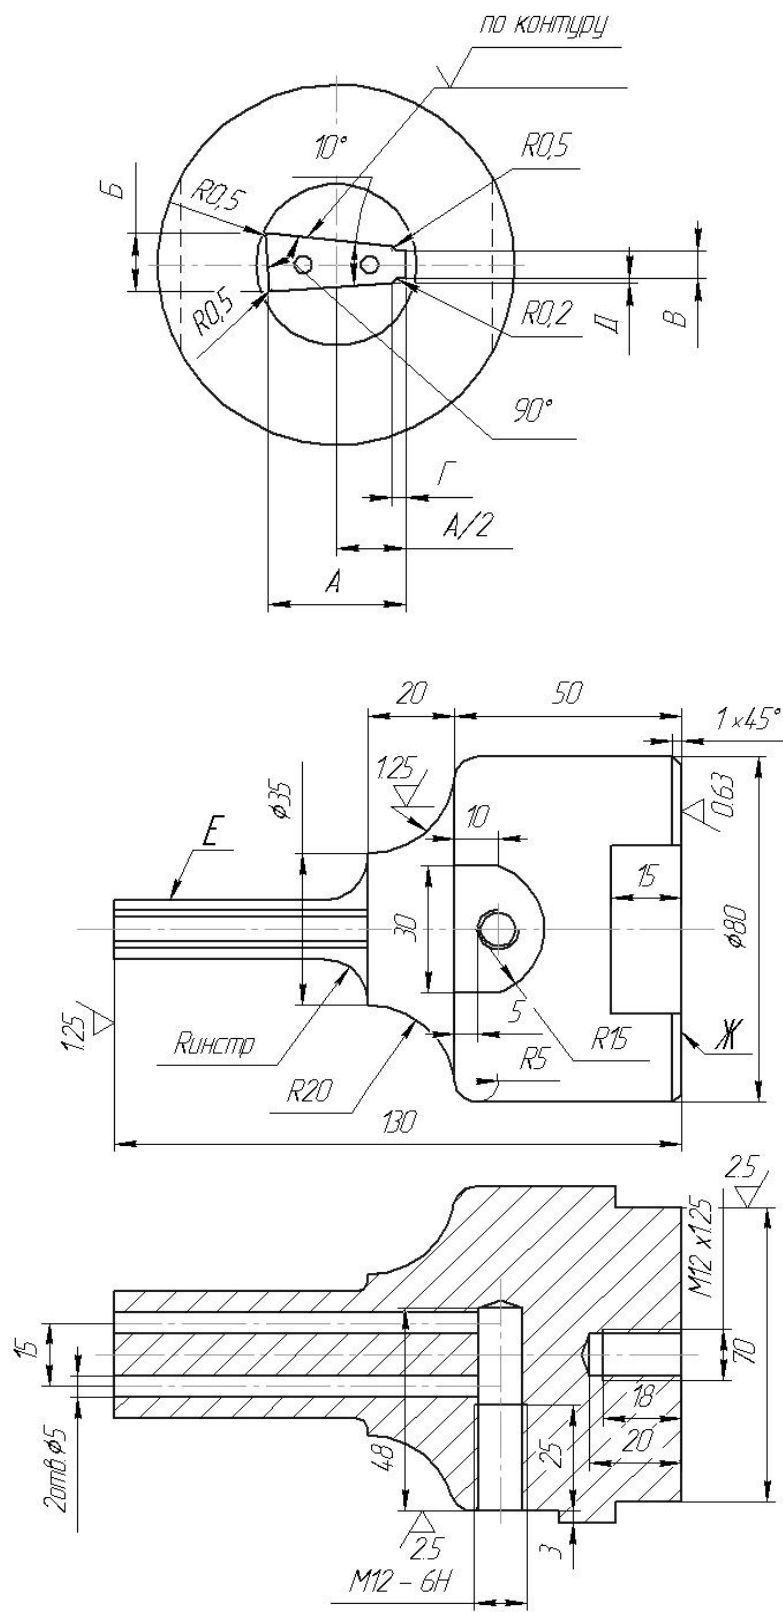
Концентратор-инструмент для изготовления матрицы вырубного штампа
